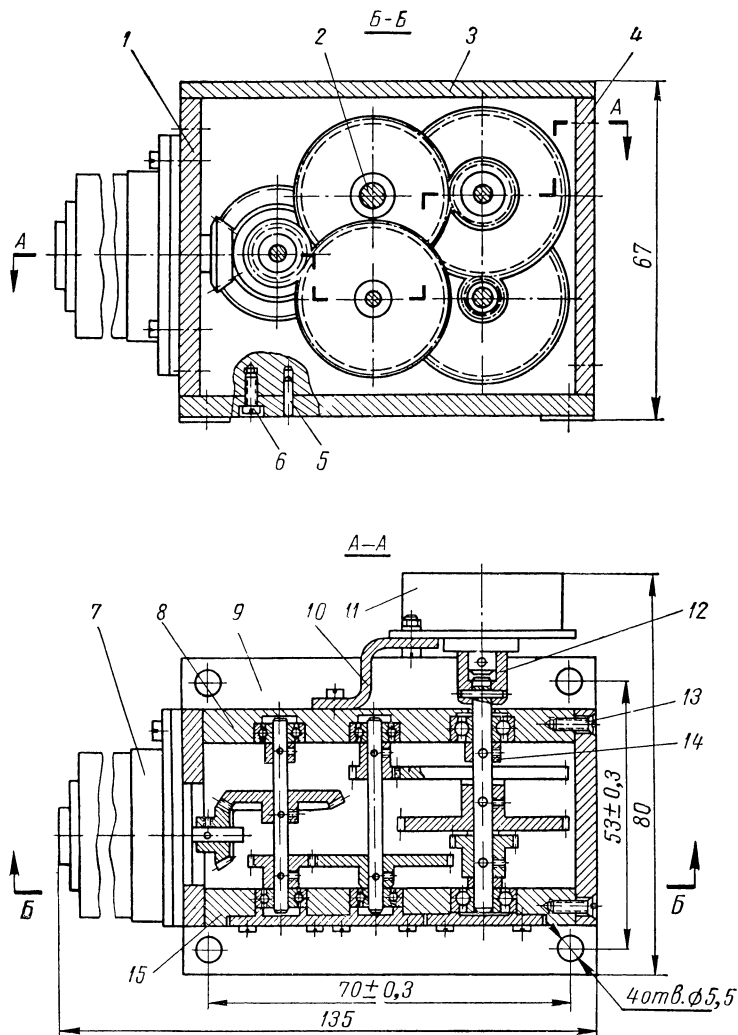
Конструкция редуктора в закрытом сборном корпусе
